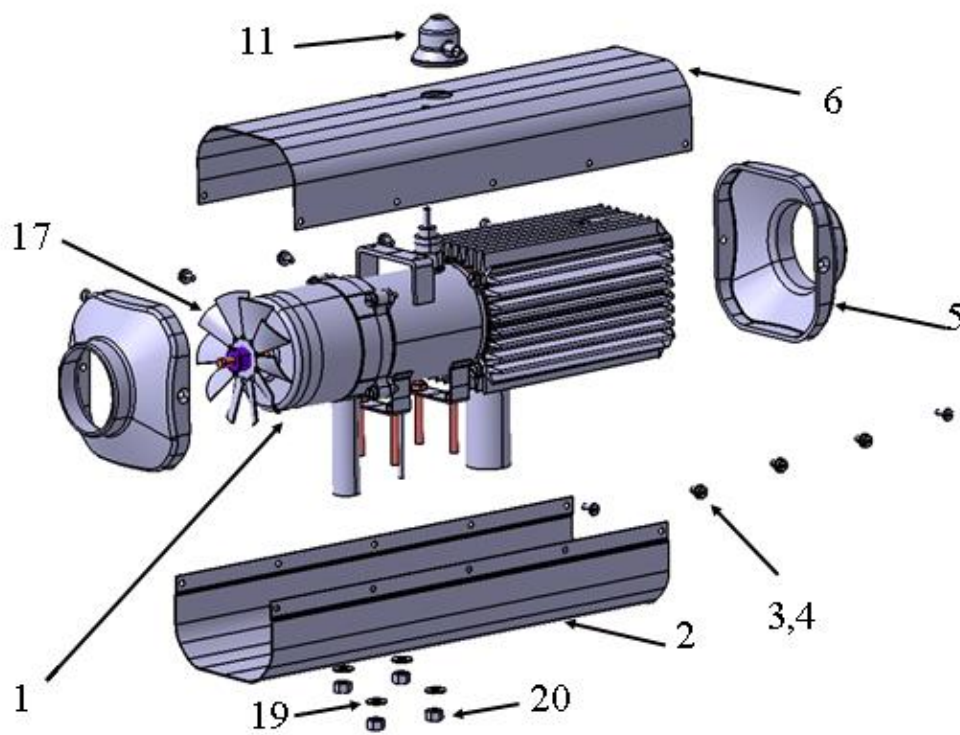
Desen generator de aer cald propriu-zis 3D explodat
